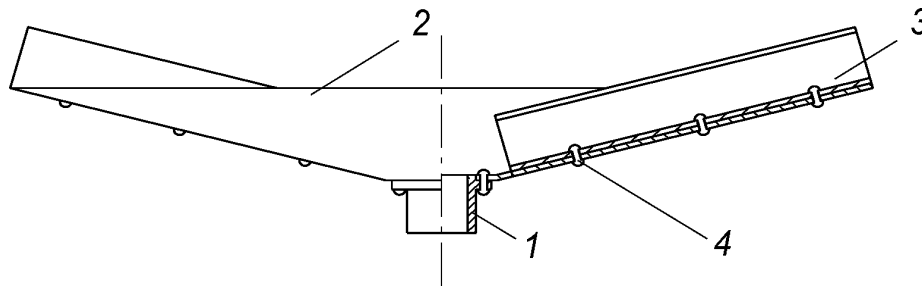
Конструкція дисково-рокидного апарата конічної форми:
